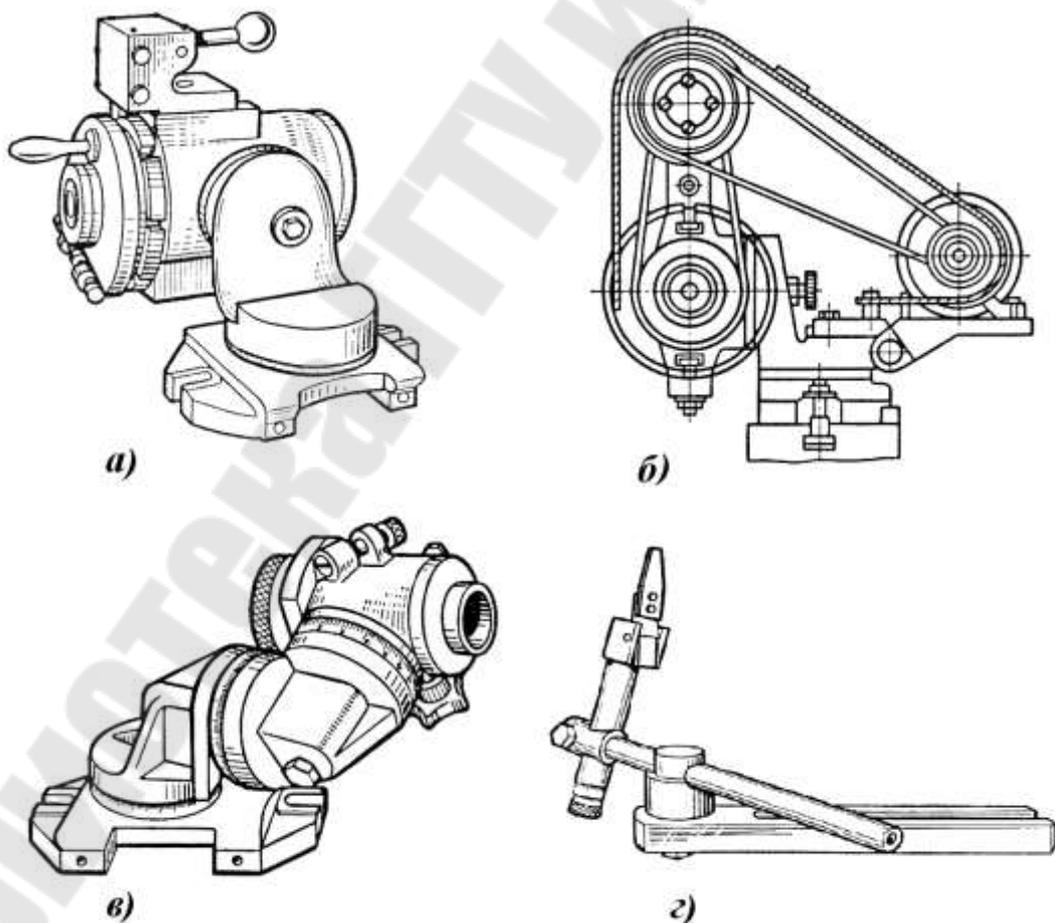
Большая универсальная головка (а); приспособление для круглого шлифования (б); малая универсальная головка (в); универсальная упорка (г).
